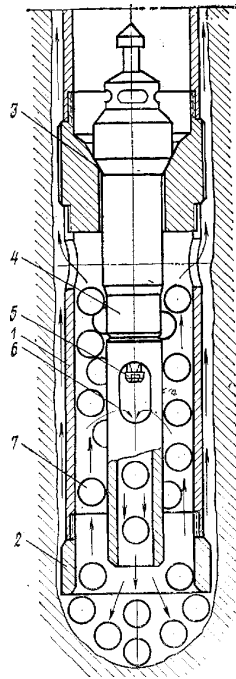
Шароструйно-эжекторный буровой снаряд с механическим вооружением лопастного типа: 1 – корпус; 2 – породоразрушающий опорный башмак; 3 – гнездо; 4 – струйный аппарат; 5 – сопло; 6 – камера смешения с окнами; 7 – шары
